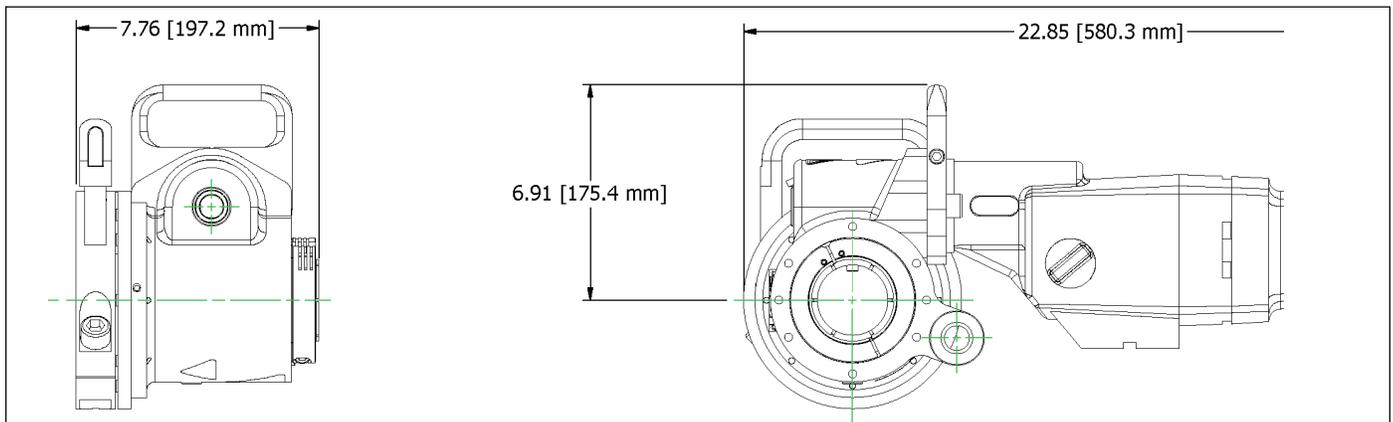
DIMENSIONES DEL MOTOR EIBENSTOCK Y DE LA RDU
